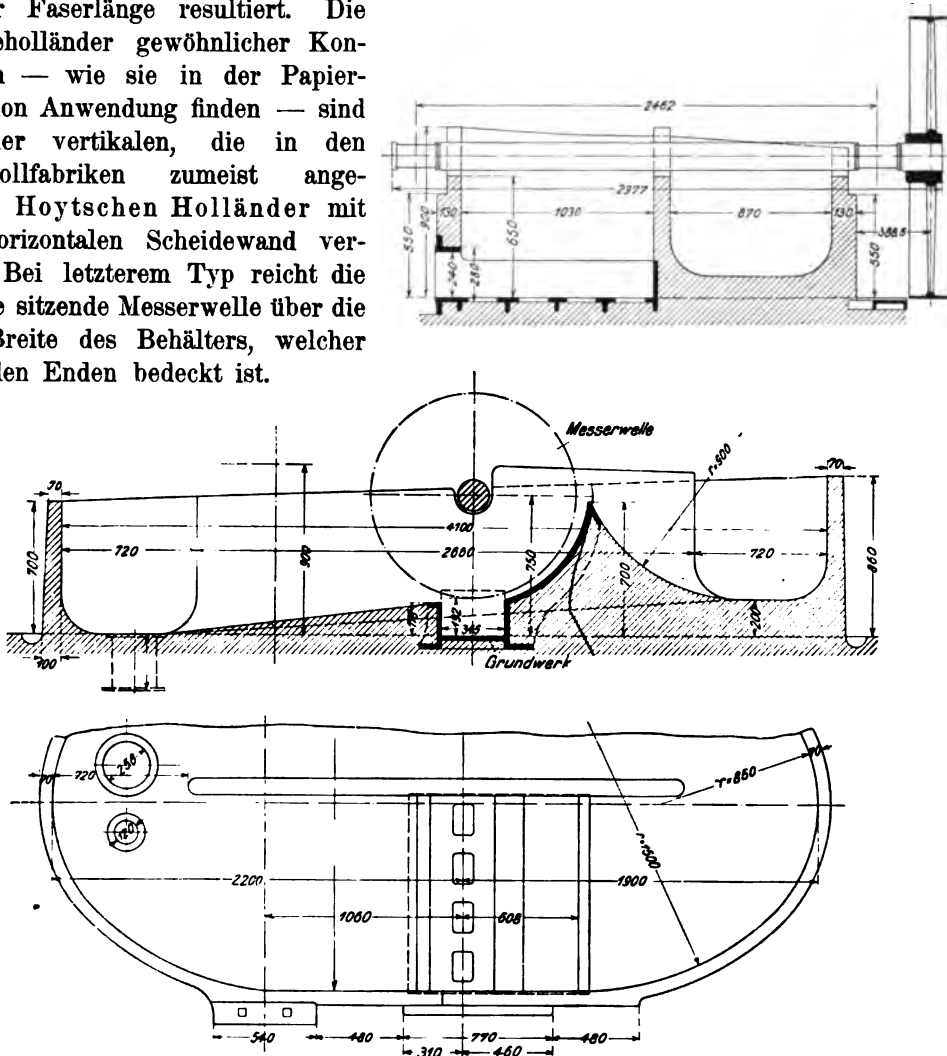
Mahlholländer für die Papierfabrik Frankenthal.
